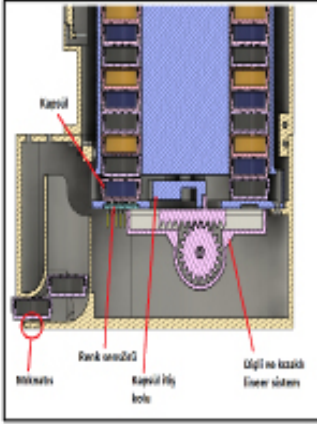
İlaç Kapsül Hazneleri ve diğer iç parçaları
